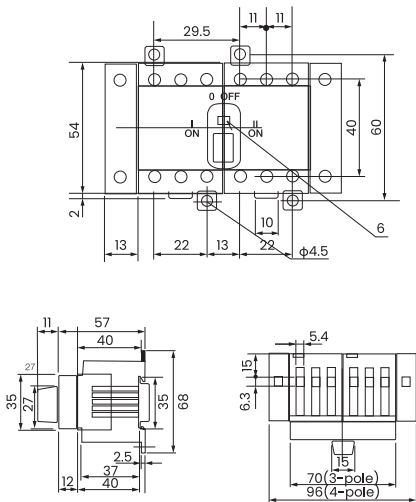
Габаритные и установочные размеры реверсивных рубильников 40А 3Р-4Р
